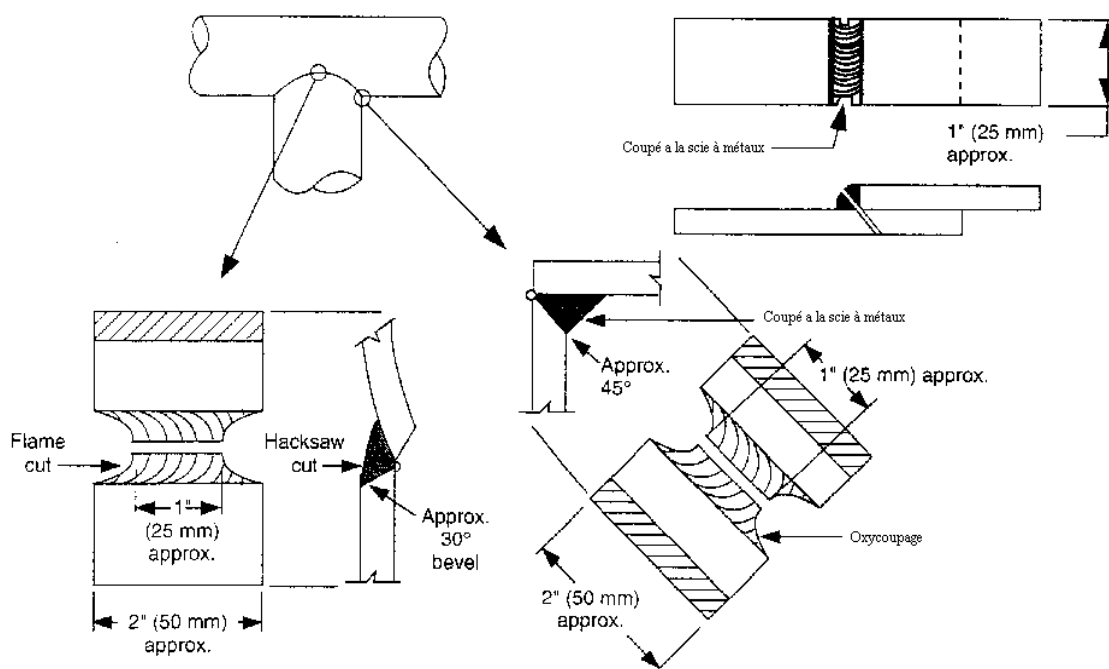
Emplacement des éprouvettes d'essai de rupture avec entaille : soudures d'essai de qualification des soudeurs et du mode opératoire pour les soudures d'angle, y compris l'essai de qualification des soudeurs sur tubes de même dimension et piquages
